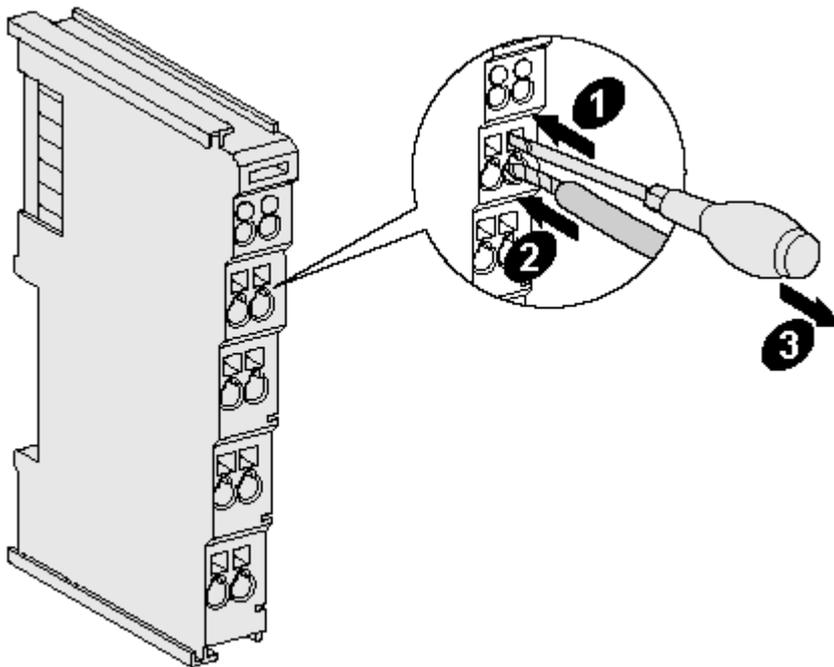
Befestigung einer Leitung an einem Klemmenanschluss
